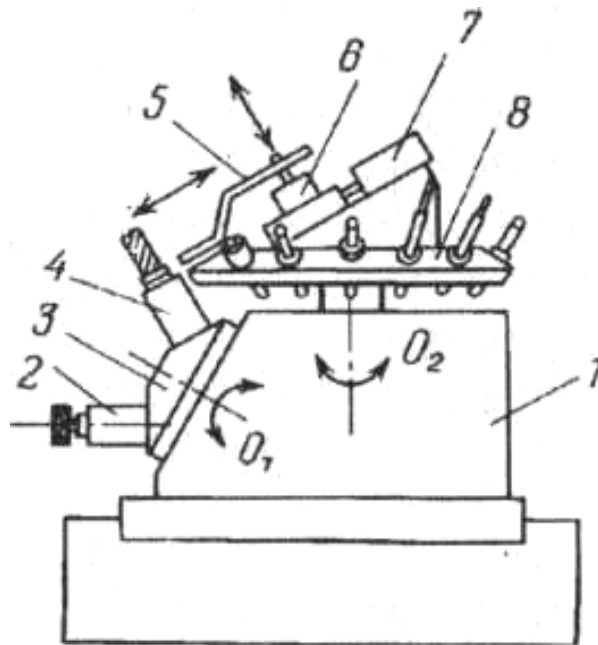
Пристрій автоматичної заміни інструменту з револьверною головкою і автооператором
